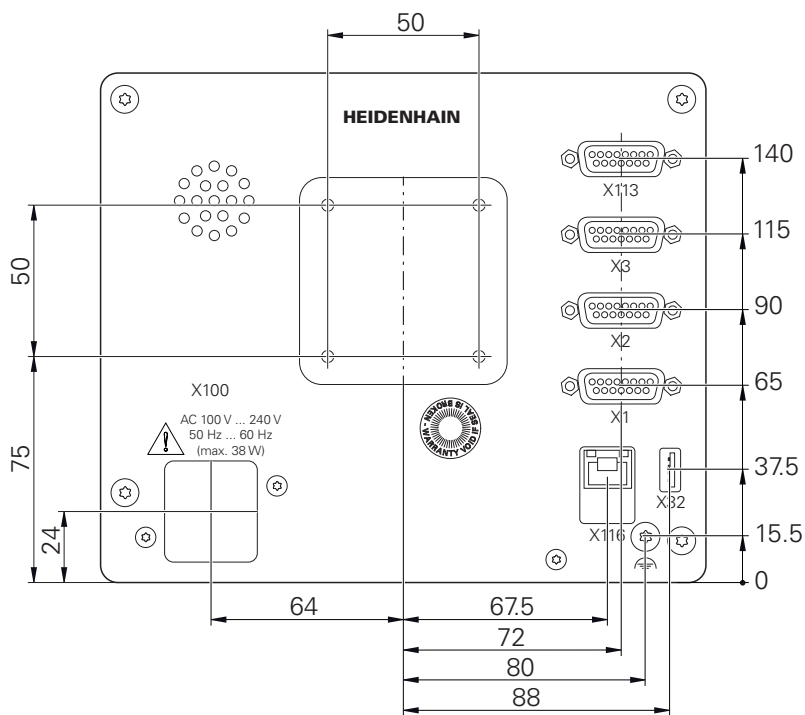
Dimensionering av enhetens baksida för enheterna med ID 1089181-xx
